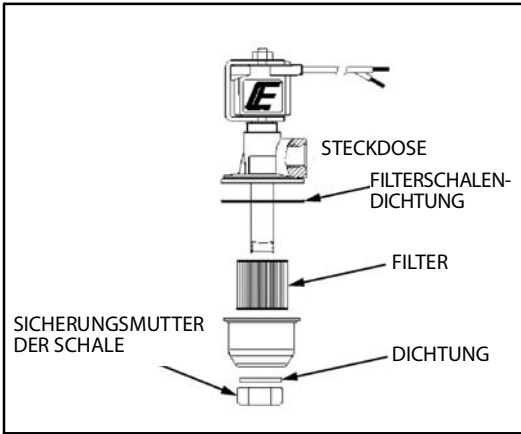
Kubota-Filter-sperrbaugruppe
